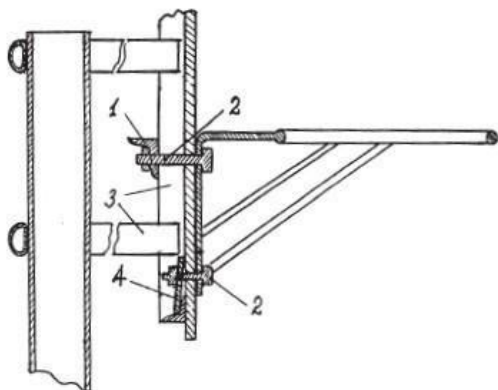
Схема крепления усиленного и стандартного кольца к старой стойке (арматуре): 1 - уголок; 2 - болты; 3 - рама; 4 - планка
